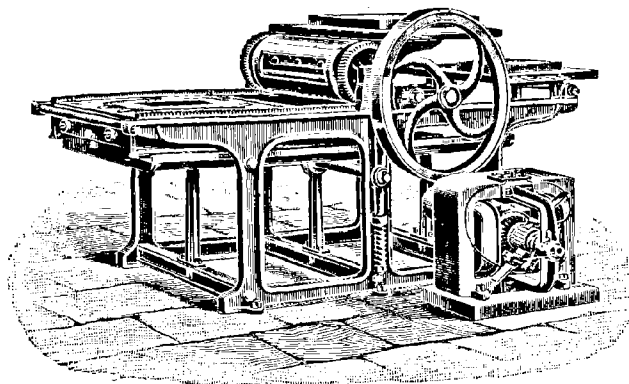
Machine à imprimer commandée par un électromoteur Fabius Henrion.
